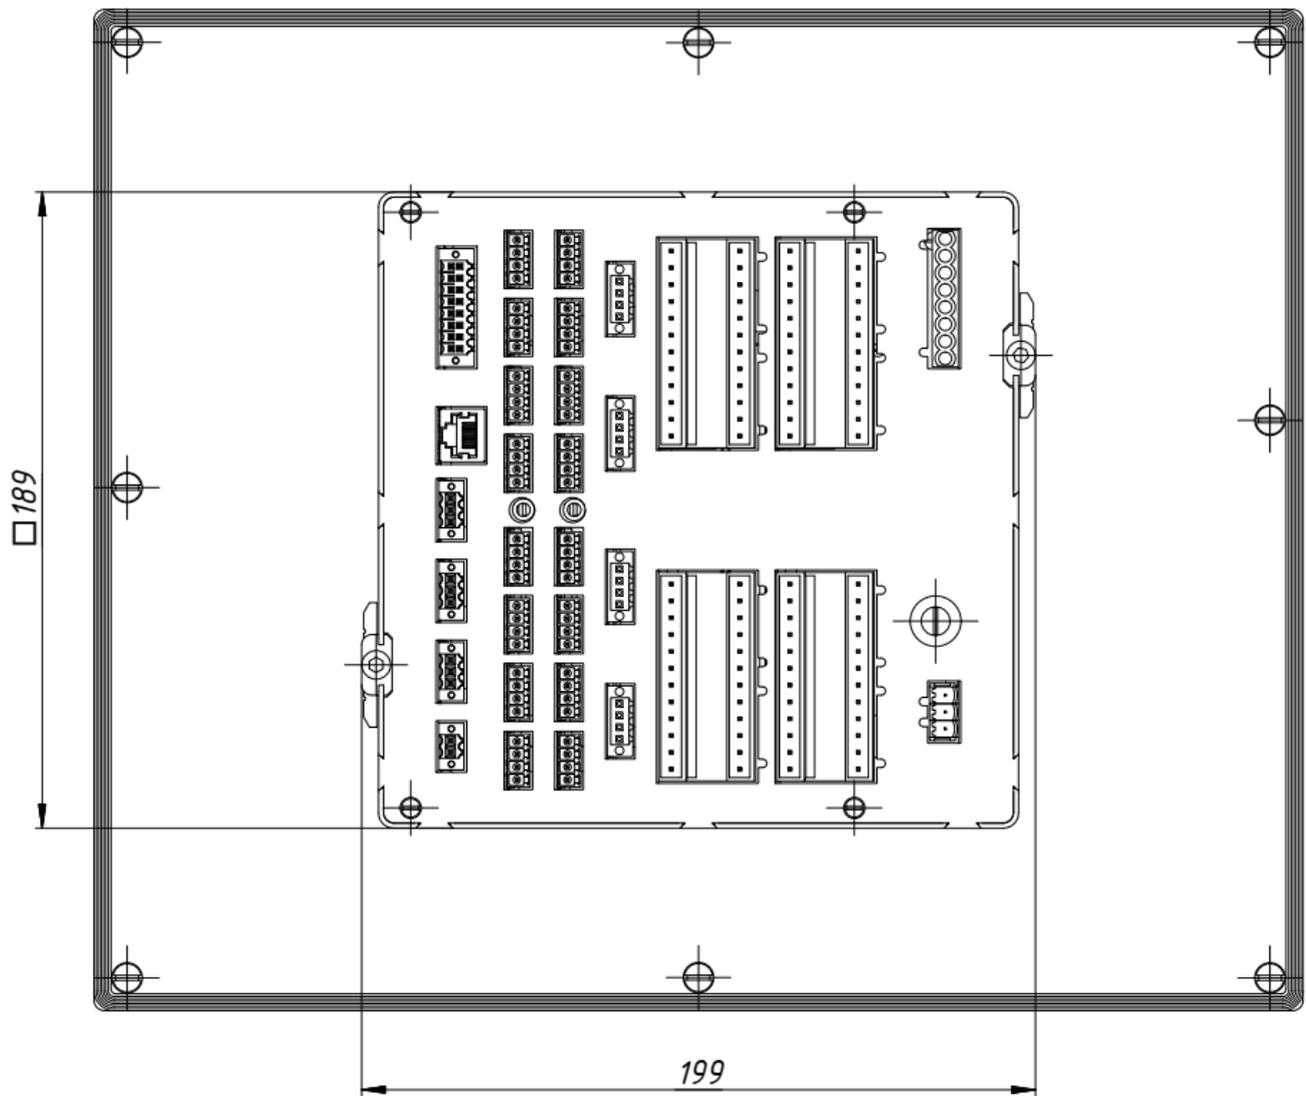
Габаритный чертёж прибора в исполнении Ф1772–3, вид сзади
